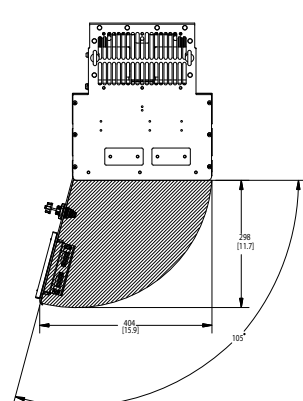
Пространство перед корпусом типа IP21/IP54, типоразмеры D1h, D5h и D6h.
